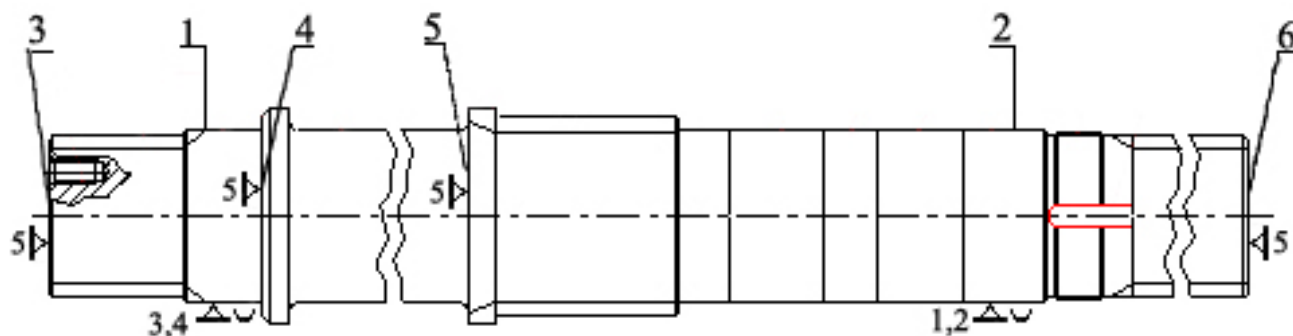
Можливі варіанти для схеми базування при фрезеруванні паза.
